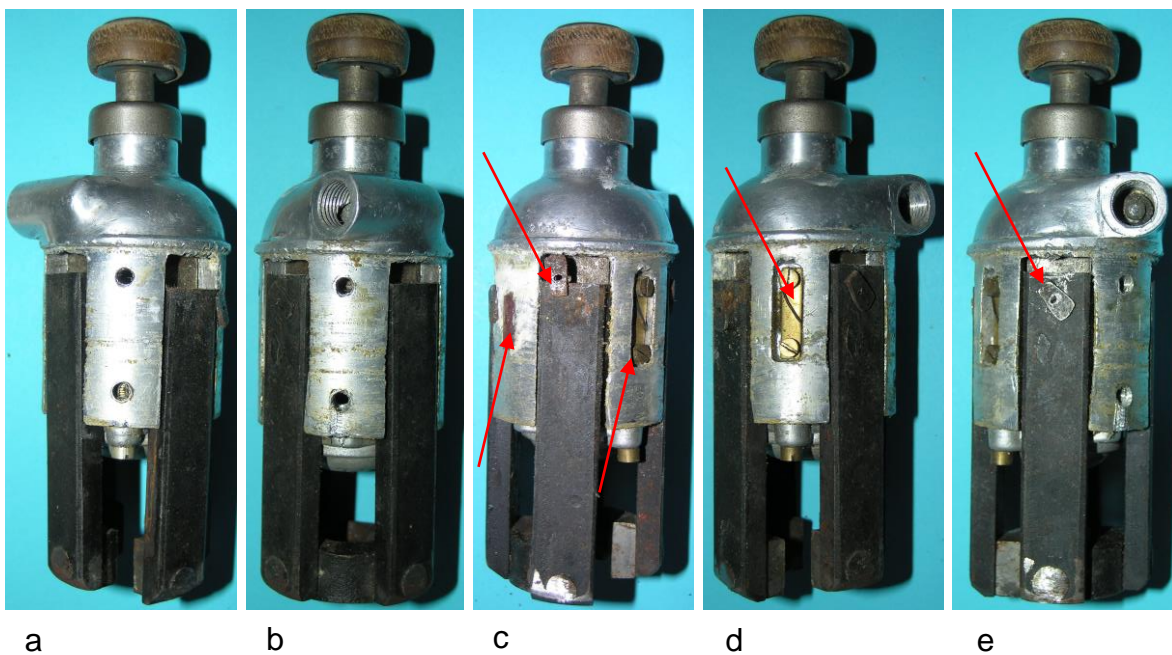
Erregersystem: a) und b) Schienen mit den Gewindebohrungen für die Befestigung der Kippvorrichtung, c) Kammern zur Fixierung der Spulenanschlüsse, d) Masseanschluss, e) Keil für die Minimierung des Luftspalts zwischen dem Magnetstab und dem Polschuh
